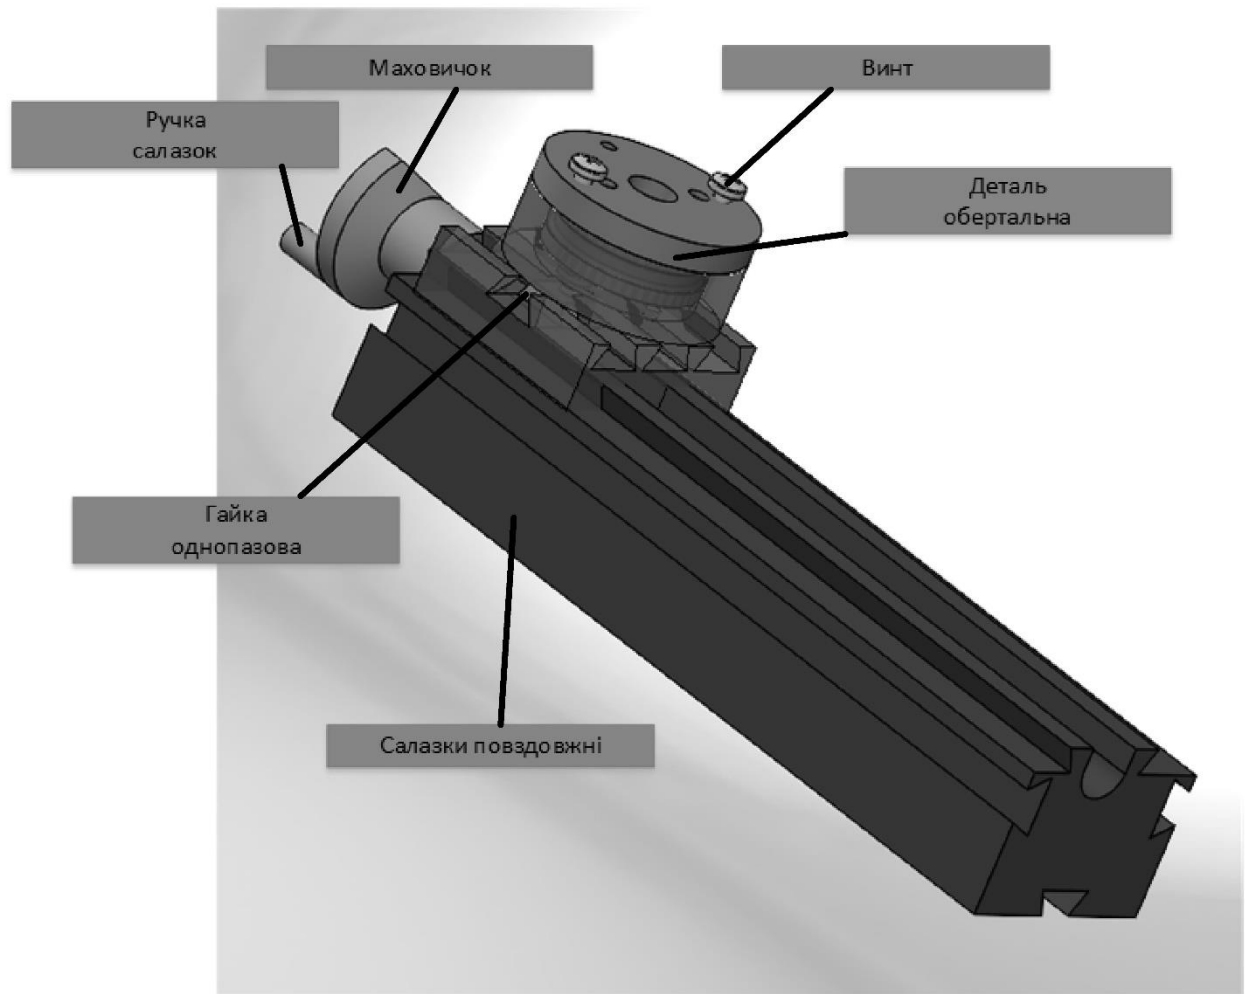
Свердильний модуль без поперечних салазок
